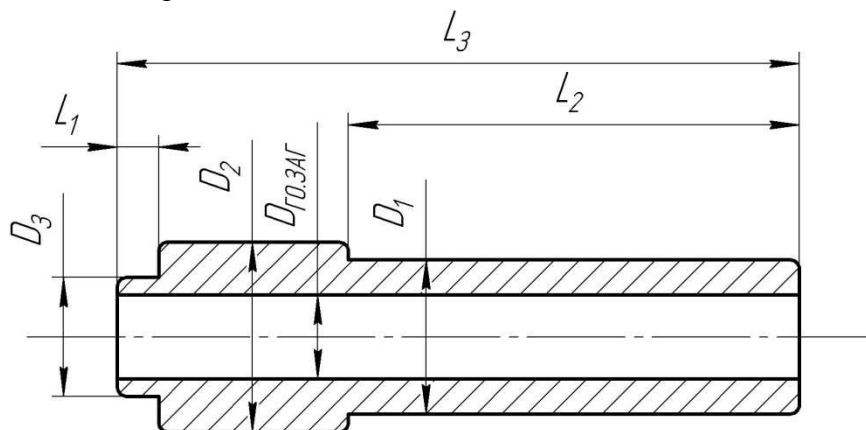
Групповой чертеж обрабатываемой заготовки – поковки детали «Цилиндр»
